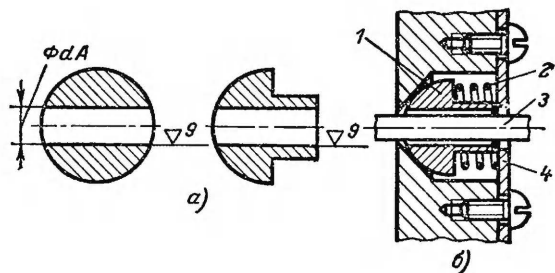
Самоустанавливающиеся подшипники скольжения.
